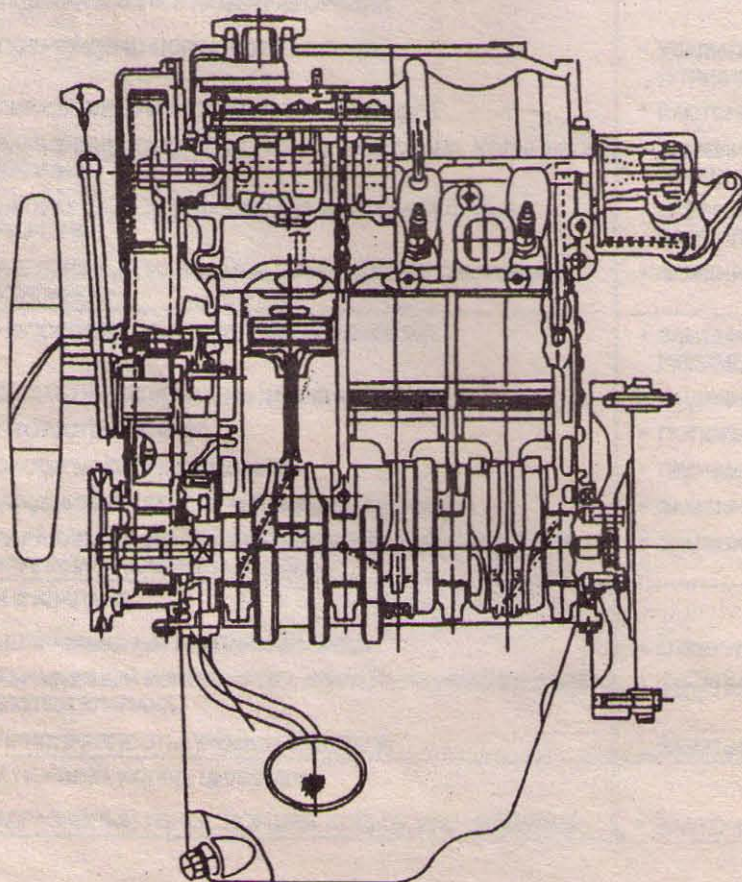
А—1 ОБЩИЙ ВИД ДВИГАТЕЛЯ
